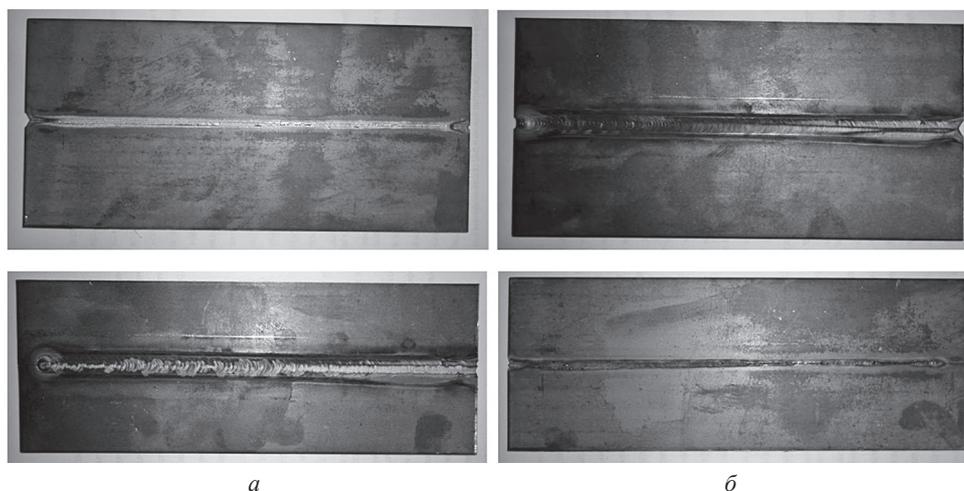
Образцы сварных швов, полученные на стыкосварочной установке АФР: а – сварка на токе 140А, $V = 1$ мм/с; б – сварка на токе 140А, $V = 1$ мм/с, с отжигающим проходом 15А, $V = 1$ мм/с
